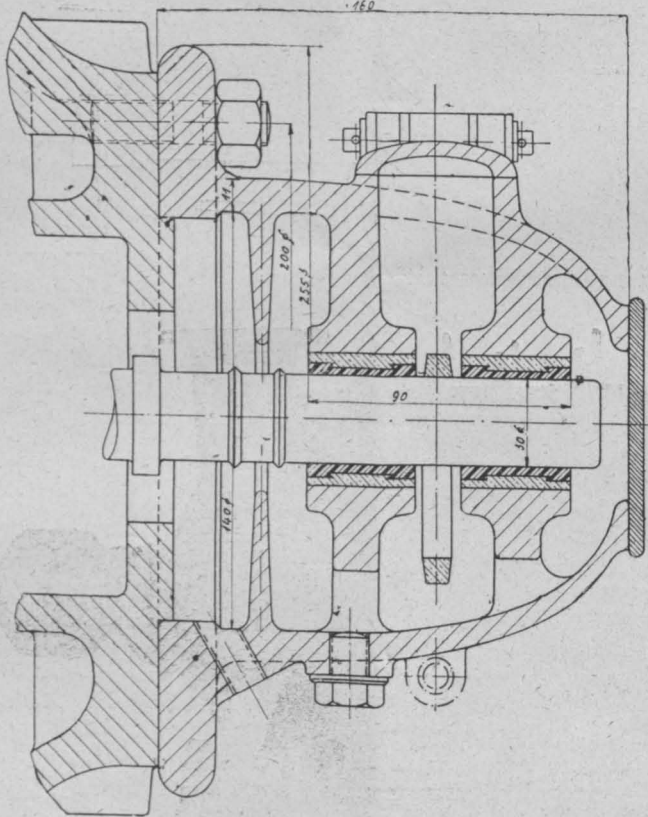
Enddrucklager der Pumpe von Kugel-Gelpcke
